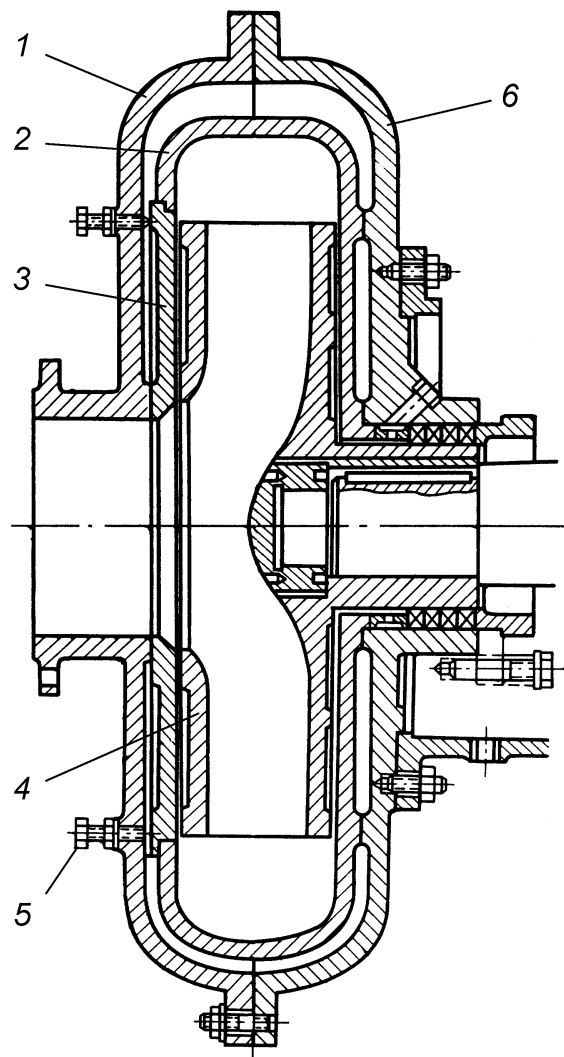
Корпус ґрунтового насосу 12GrТ-8: 1 – передня половина корпусу; 2 – внутрішній корпус; 3 – бронедиск; 4 – робоче колесо; 5 – притискний болт; 6 – задня половина корпусу
